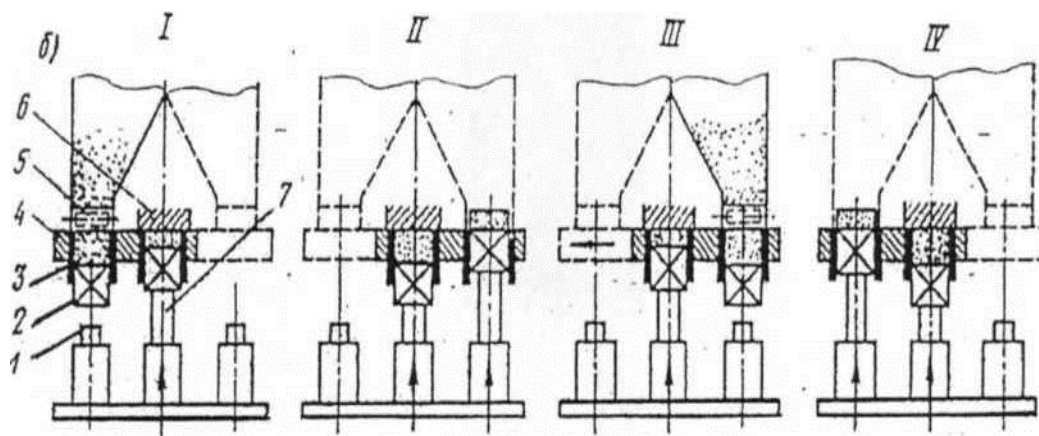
Принципиальная схема гидравлического пресса «Крупп-Интертехник»: 1- выталкивающий плунжер; 2 - штамп; 3-пресс-форма; 4-стол загрузочный ящик; 6-контрштамп; 7- прессующий плунжер: I - заполнение смесью левой пресс-формы, формование сырца правой; II - начало формования в левой пресс-форме, выпрессовка и съем сырца из правой; III –заполнение смесью правой пресс-формы, окончание формования левой; IV - выпрессовка и съем сырца с левой пресс-формы, начало формования в правой.
